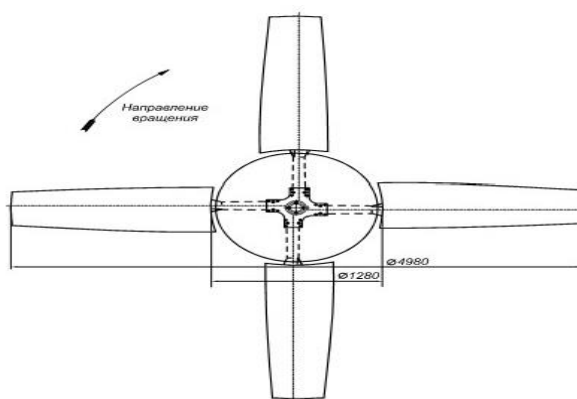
Стеклопластиковое рабочее колесо типа ГАЦ-50-4М2
